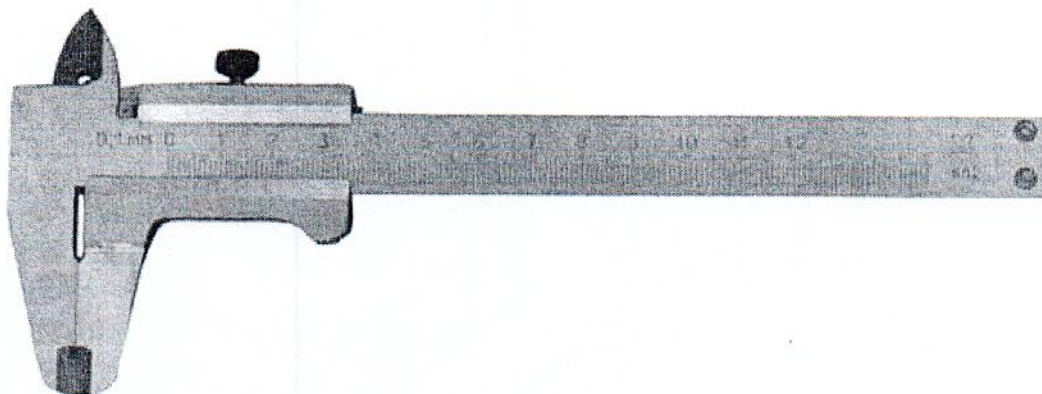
Внешний вид штангенциркуля типа ШЦ-I
